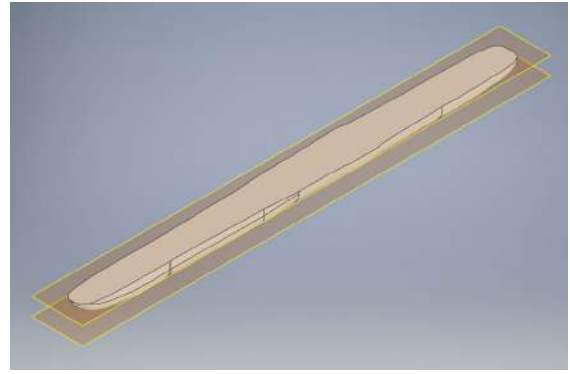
Plano de corte del ensamblaje de la cabina con los flotadores ubicado a 160 mm. Fuente: Elaboración propia.
